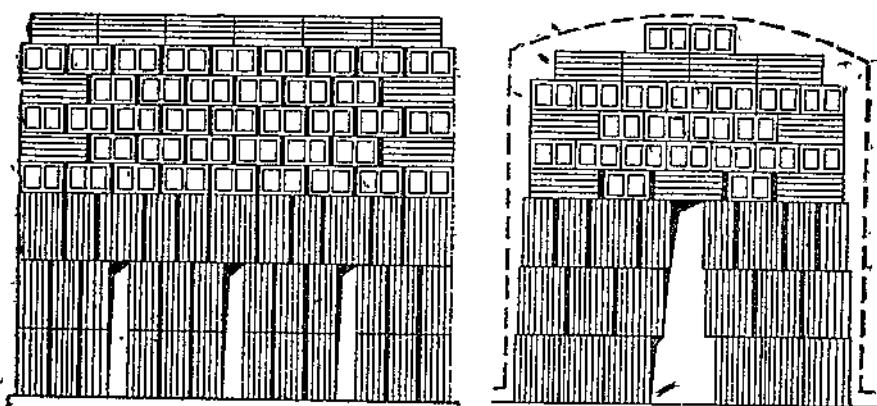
Садка пустотелых блоков в тоннельной печи.
